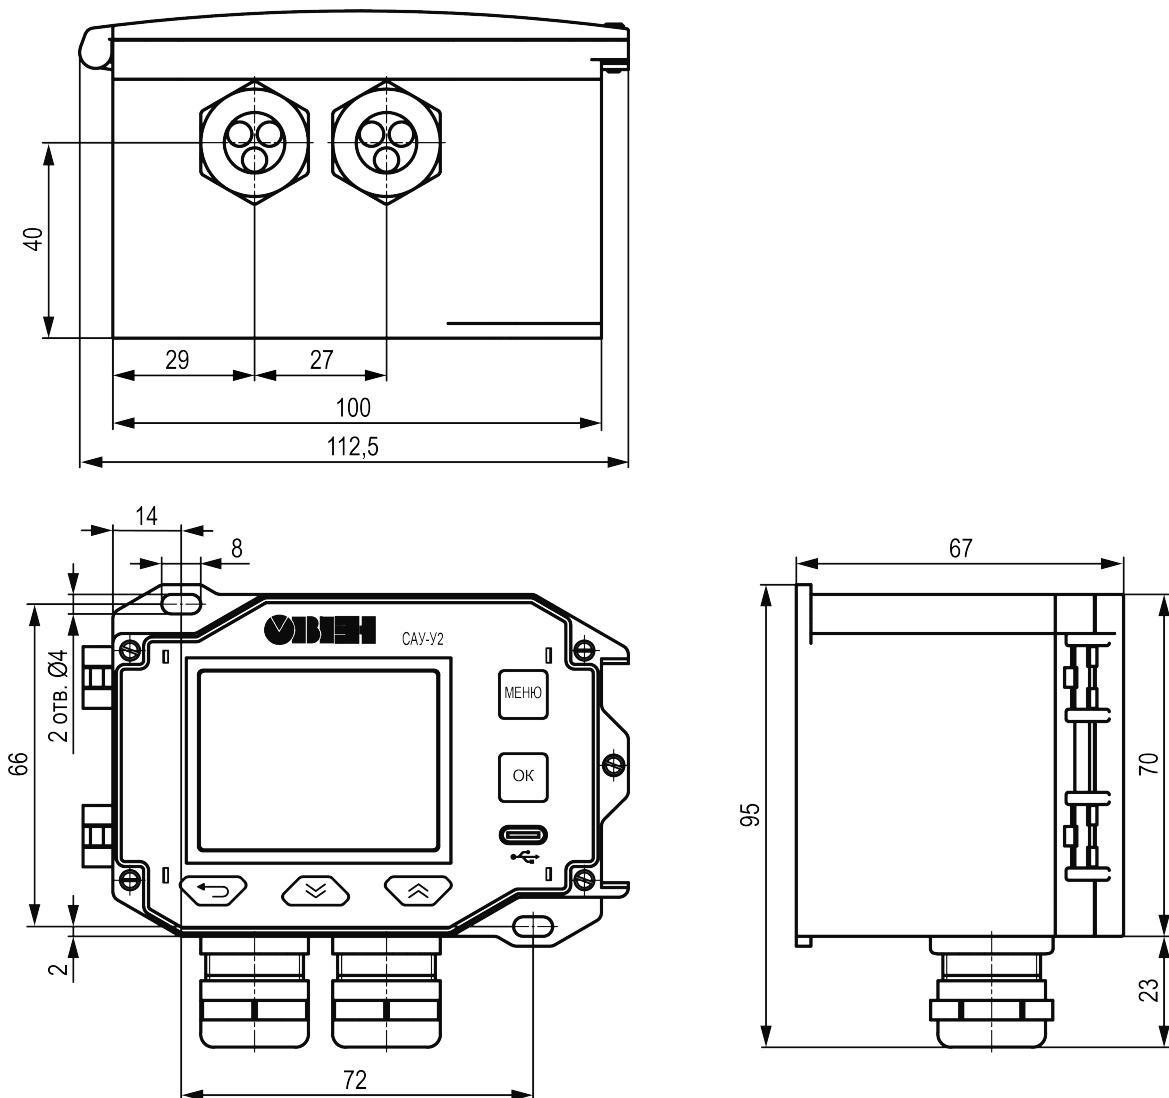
Габаритные и присоединительные размеры САУ-У2-Н4
